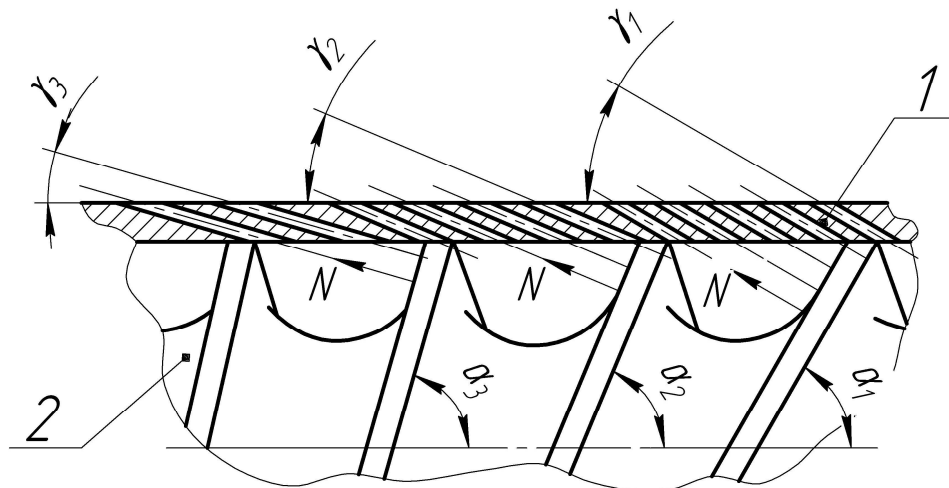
Схема расположения отверстий в перфорированной втулке шнекового узла отжатия обвалочного пресса.
